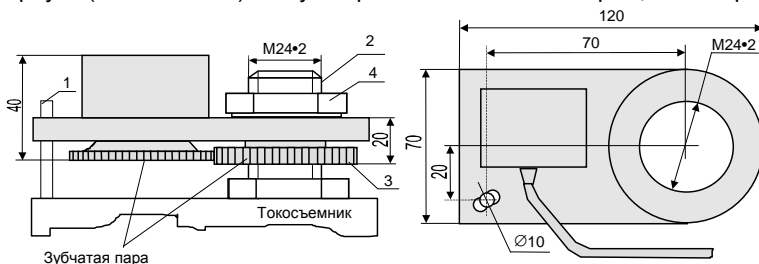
Установка датчика угла поворота платформы (азимута)
